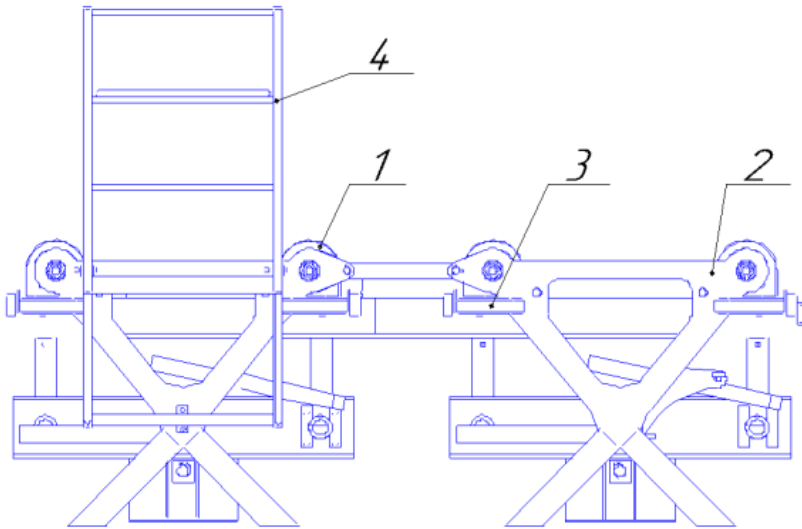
Изометрия противовесной тележки: 1 – Опорные катки; 2 – Сварная рама; 3 – Направляющие катки; 4 – Лестница
